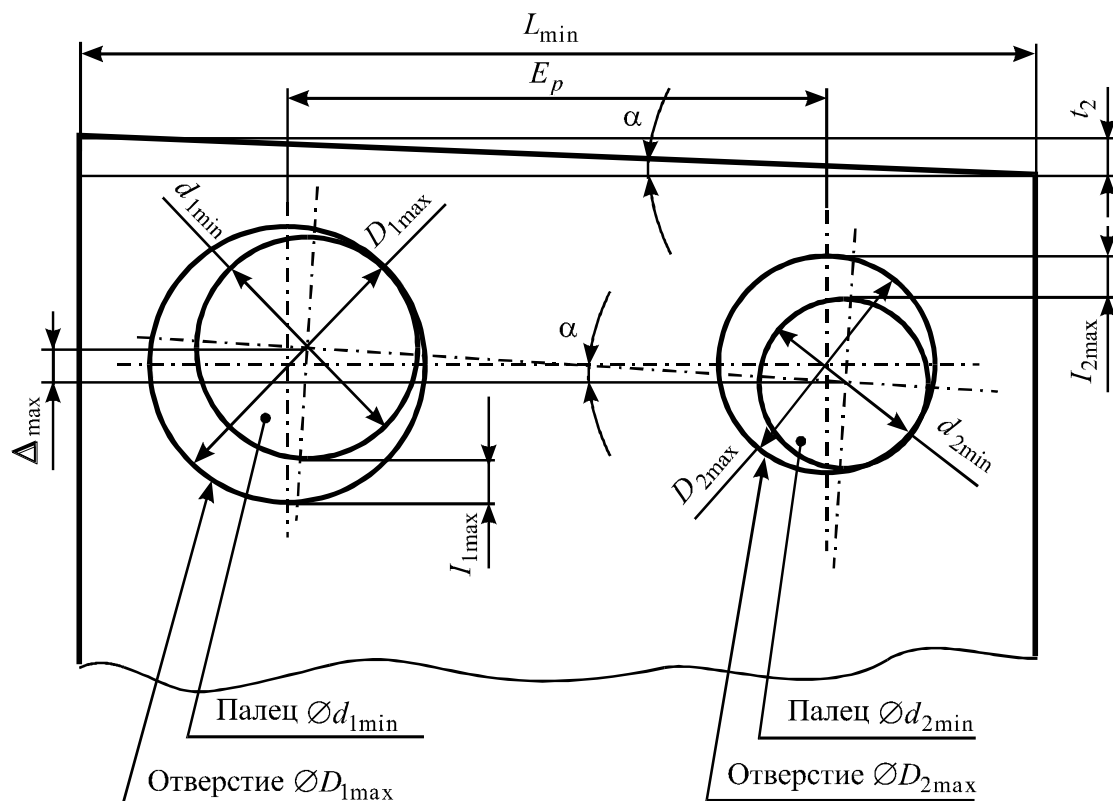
Схема расположения заготовки и пальцев приспособления, из которой следует особенность влияния допуска параллельности t_2 на смещение осей Δ_{\max}
